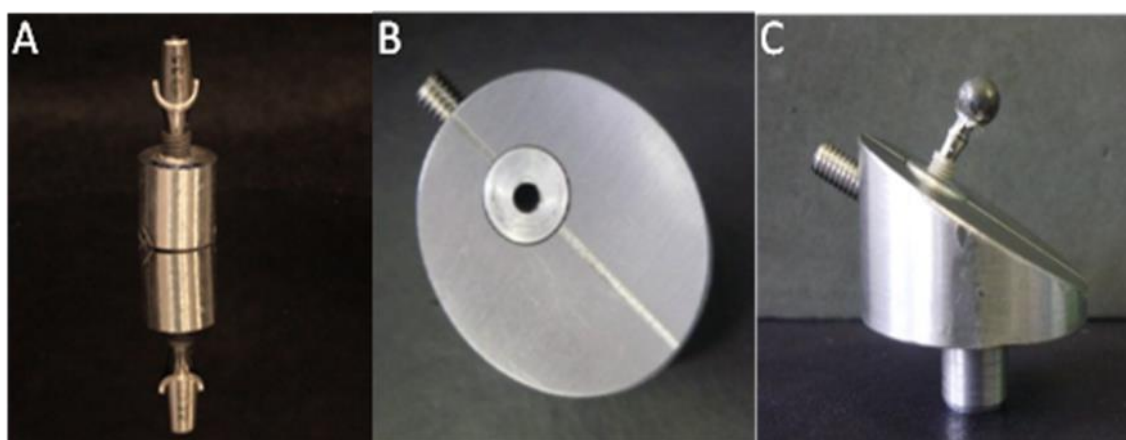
A- Conjunto implante/pilar anatômico montado no *stub* de alumínio. B- Vista superior do dispositivo de fixação do *stub* para realização do ensaio. C- Vista lateral do conjunto implante/pilar reto/esfera metálica, montado no dispositivo.
